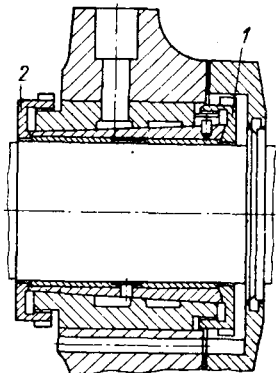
Подшипники скольжения для цилиндрической шейки:
